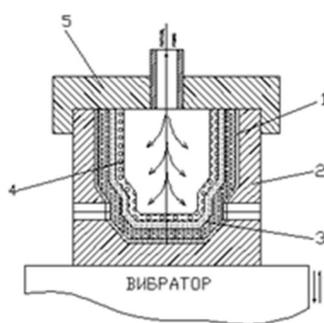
Контейнер для изготовления . 1-спекания пористая заготовка; 2-корпус контейнер; 3- слой мелкого порошка; 4- проницаемый элемент; 5- крышка.
